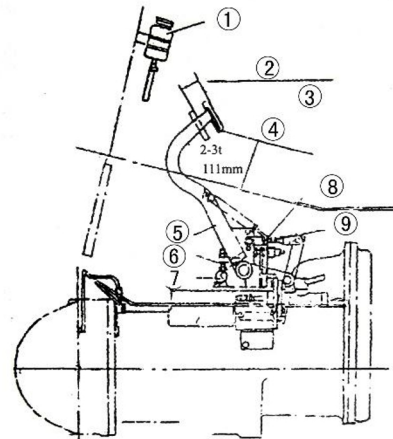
Einstellen des Bremspedals (hydraulisches Fahrzeug)
